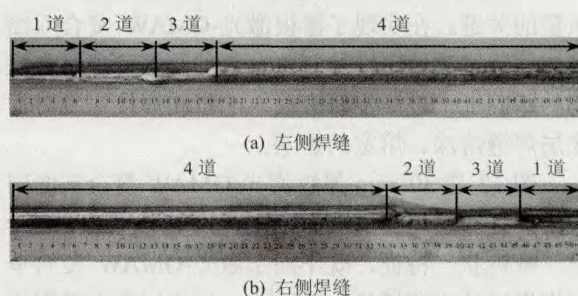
激光-GMAW 复合双面同步横焊焊缝表面形貌
